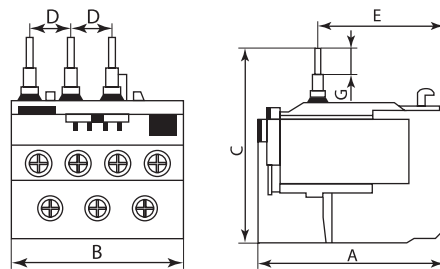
Габаритные и установочные размеры реле РТЛ-1001...РТЛ-2063
